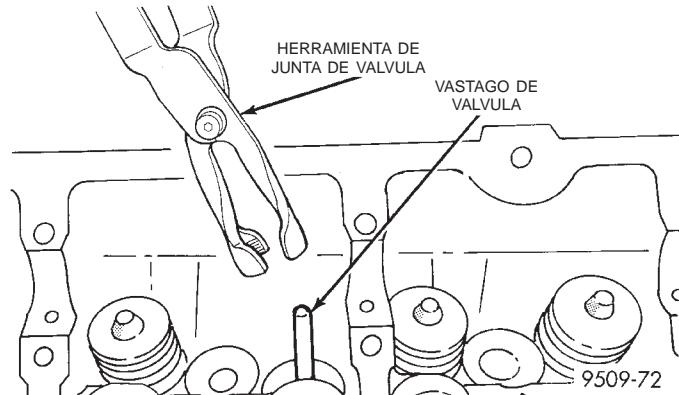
Herramienta para junta de aceite del vástago de válvula
